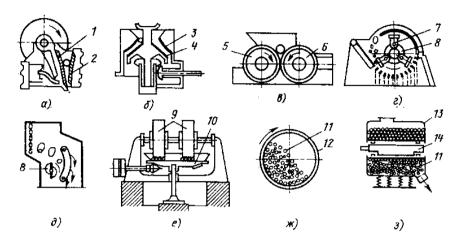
Классификация дробильно-размольного оборудования: а — щековая дробилка; б — конусная дробилка; в — валковая дробилка; г — молотковая дробилка; д — ударная дробилка; е — бегуны; ж — шаровая (стержневая) мельница; з — вибромельница тонкого помола
